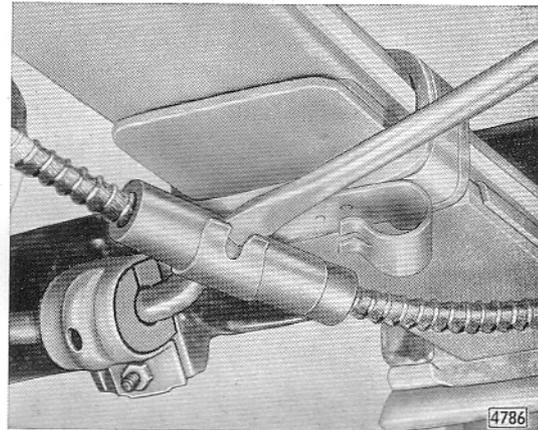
Halter an Hinterfeder für Druckschlauch des hinteren Handbremsseiles aufdrücken
